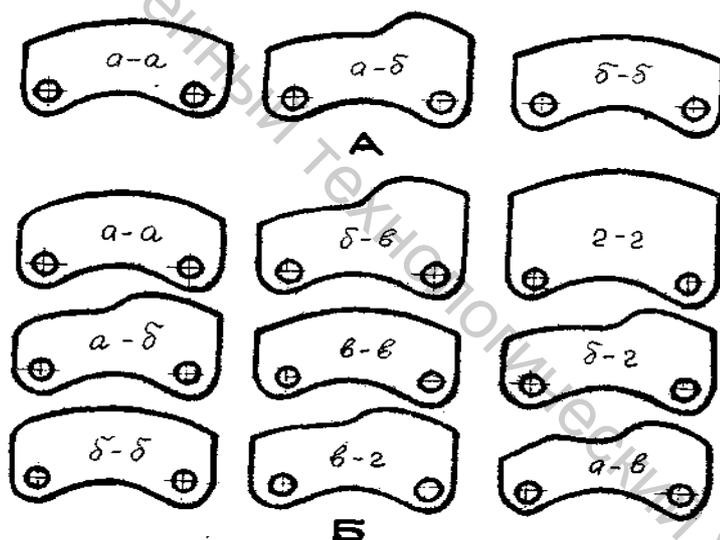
Пластины для двухуточного (а) и четырехуточного (б) приборов станков типа СТБ
